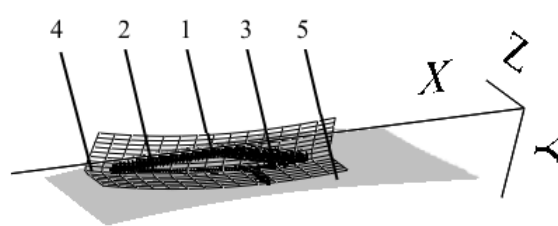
Пляма контакту фрези й кулачка розподільчого вала при обробці ділянки кулачка найбільшого радіуса
